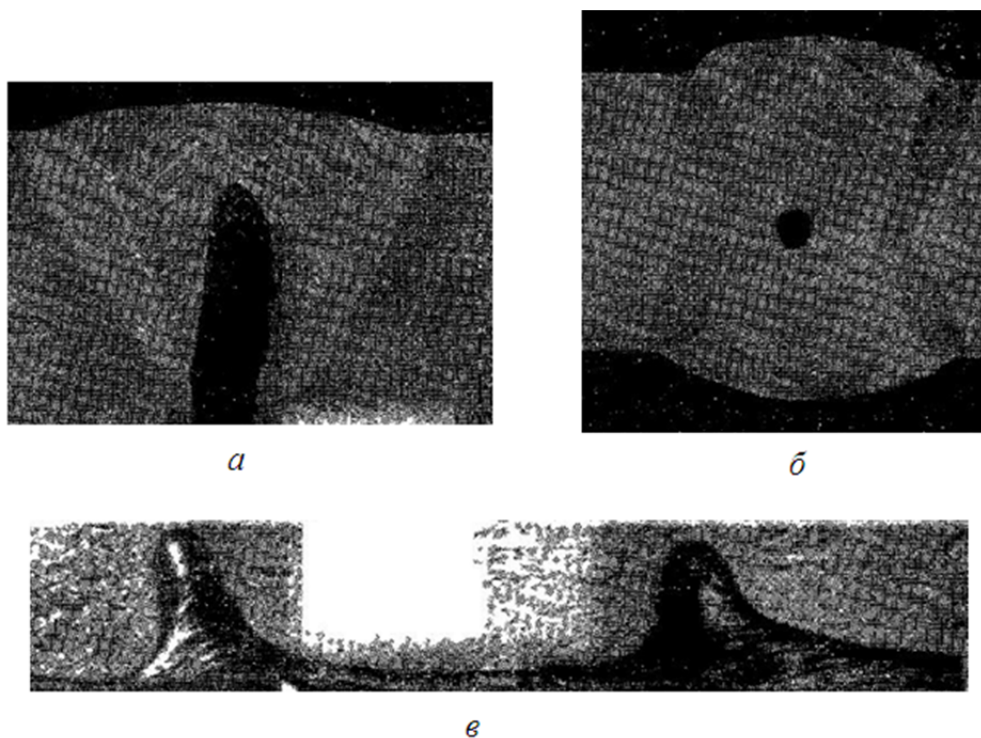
Шлакові канали: *а* — після зварювання з одного боку, розріз поперек шва; *б* — після зварювання з одного боку, розріз уздовж шва; *в* — після зварювання з двох сторін
